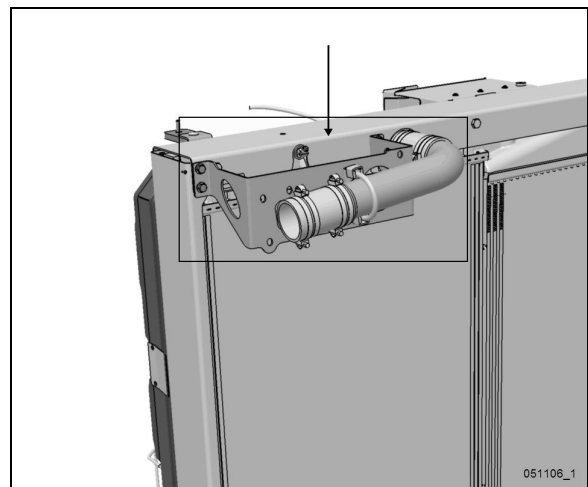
TUBO SUPERIOR & SOPORTE DEL RADIADOR INSTALADO
